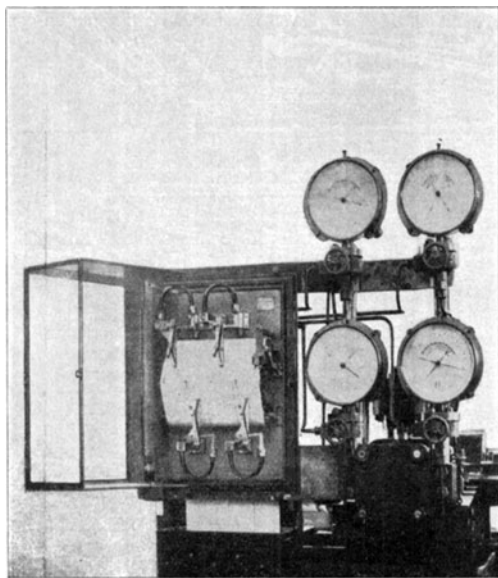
Vierfache selbstschreibende Meßdosen-Druckmeßeinrichtung des Versuchsfeldes für Werkzeugmaschinen zu Berlin für Drehbänke.
